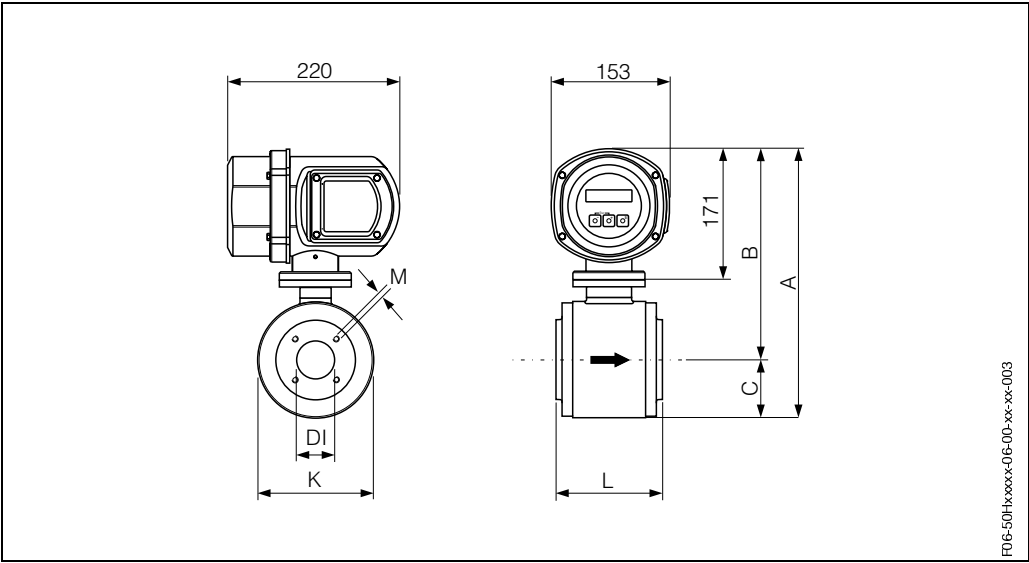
Dimensiones del Promag H / DN 40...100 (v. compacta, cabezal de acero inoxidable para montaje en campo)
